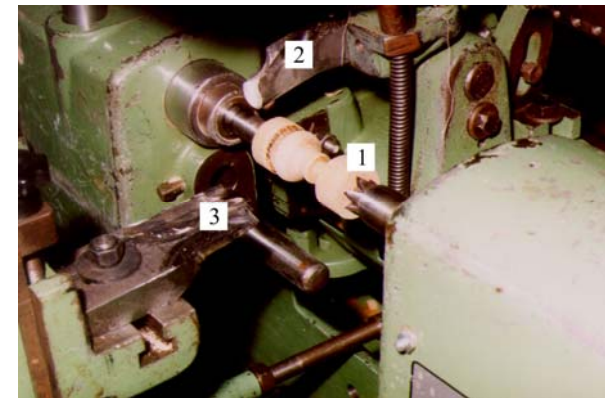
Вузол токарно-шліфувального автомату для виготовлення деталі стільця: 1) деталь; 2) різець прохідний; 3) різець фасонний
